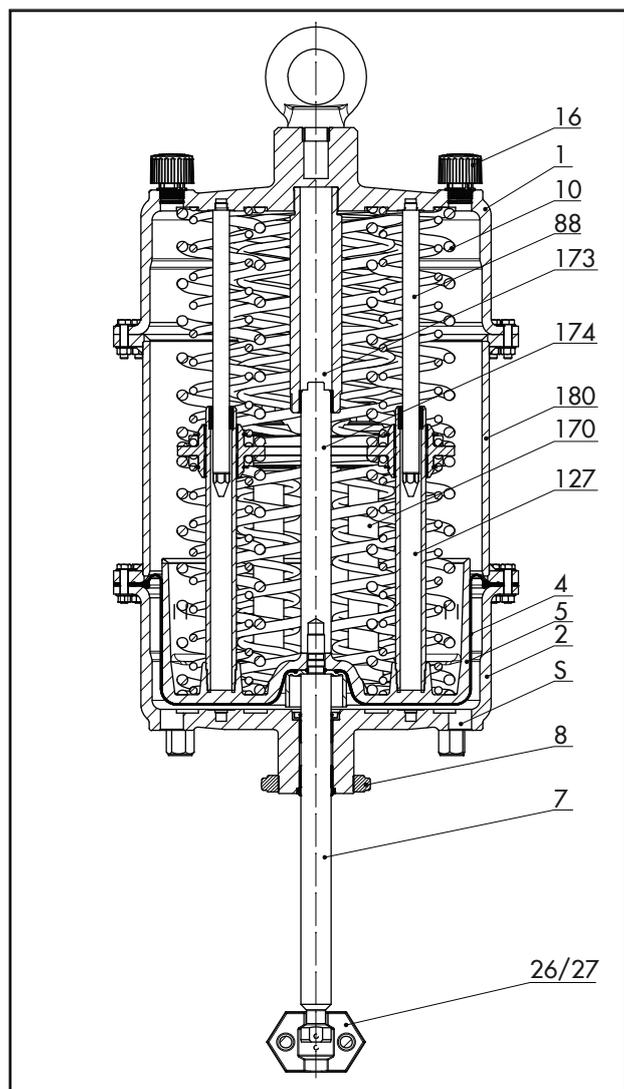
Чертёж в разрезе привода Тип 3271 1400-250 см²
